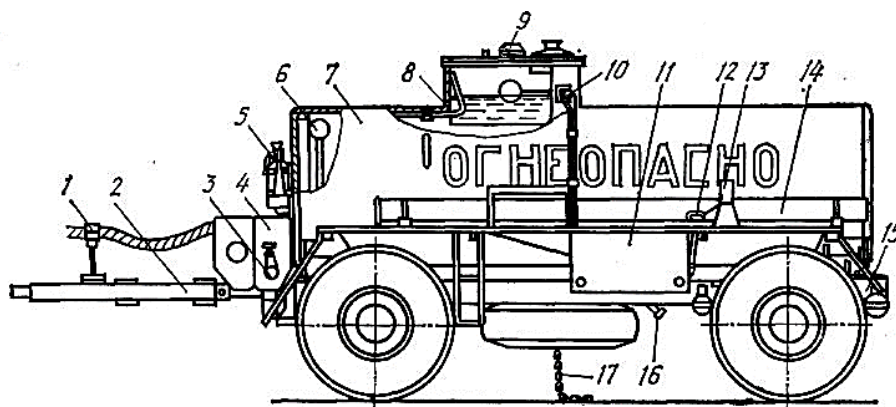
Прицеп-цистерна ПЦ-6,7-8925: 1 – опора крепления рукава; 2 – дышло прицепа; 3 – трубопровод для приема и выдачи нефтепродукта; 4 – ящик задвижки Ду-70; 5 – огнетушитель; 6 – поплавковый указатель уровня; 7 – цистерна; 8 – горловина; 9 – дыхательный клапан; 10 – ограничитель наполнения; 11 – боковой ящик; 12 – клин заземления; 13 – заземляющее устройство; 14 – пенал для рукава; 15 – шасси; 16 – трубопровод слива отстоя; 17 – цепь заземления
